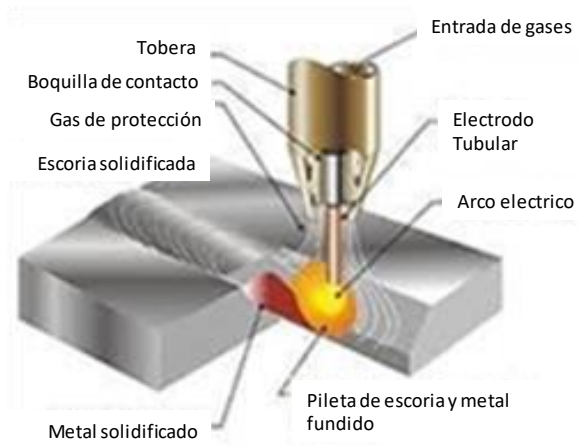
Esquema del proceso de soldadura FCAW.
